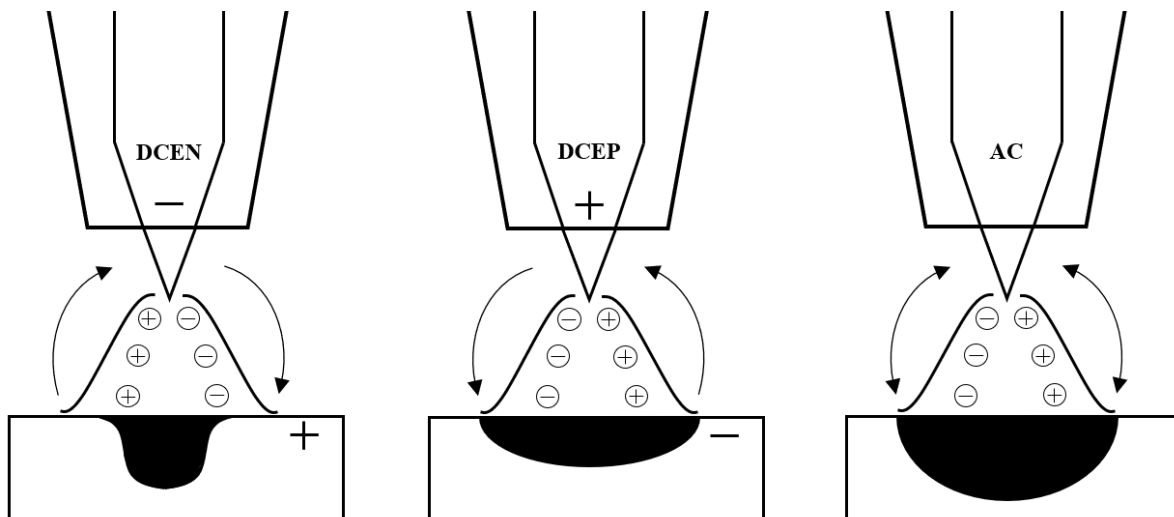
Modos de polaridad en soldadura al arco.
